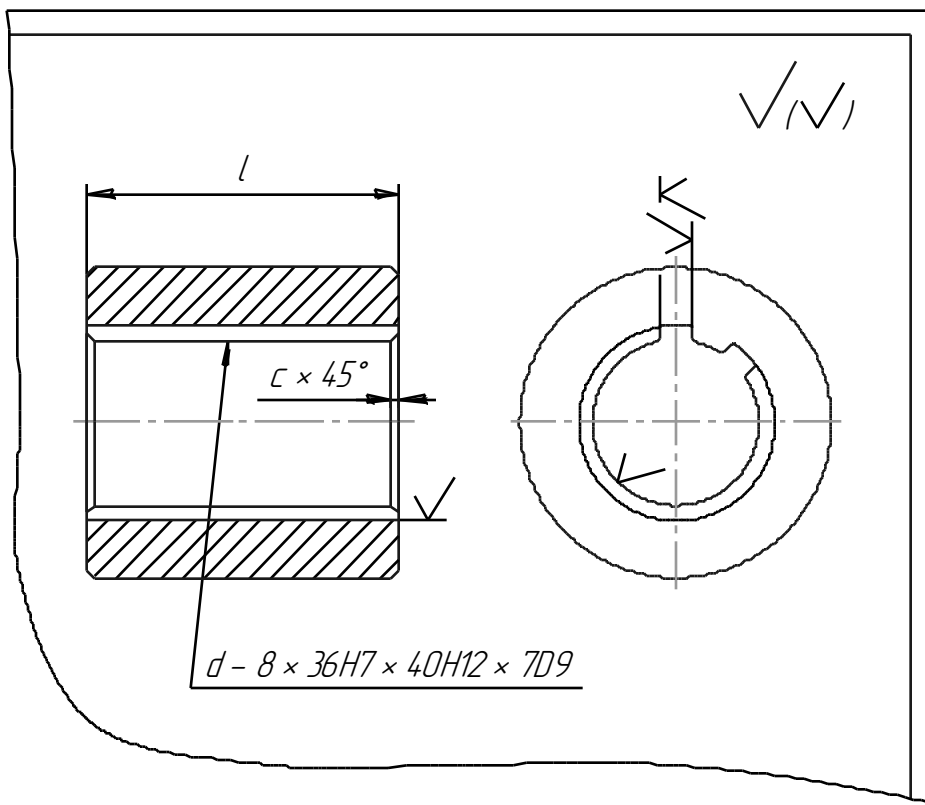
Чертеж шлицевого отверстия с прямоугольным профилем зубьев
